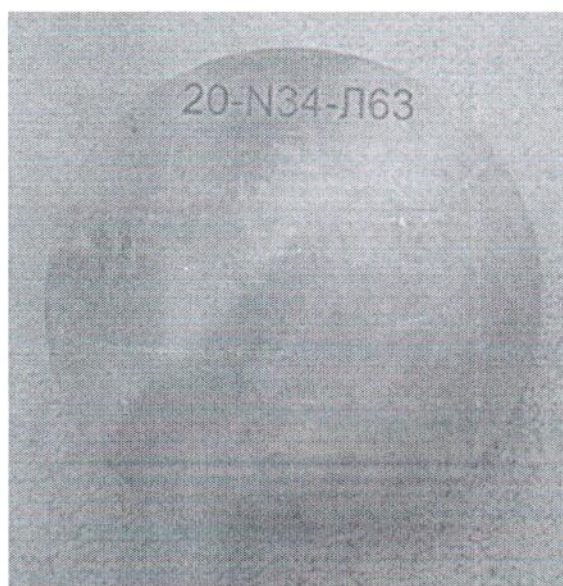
Фотография маркировки одного стандартного образца толщины КУСОТ-180 набор № 1 заводской номер № 34
